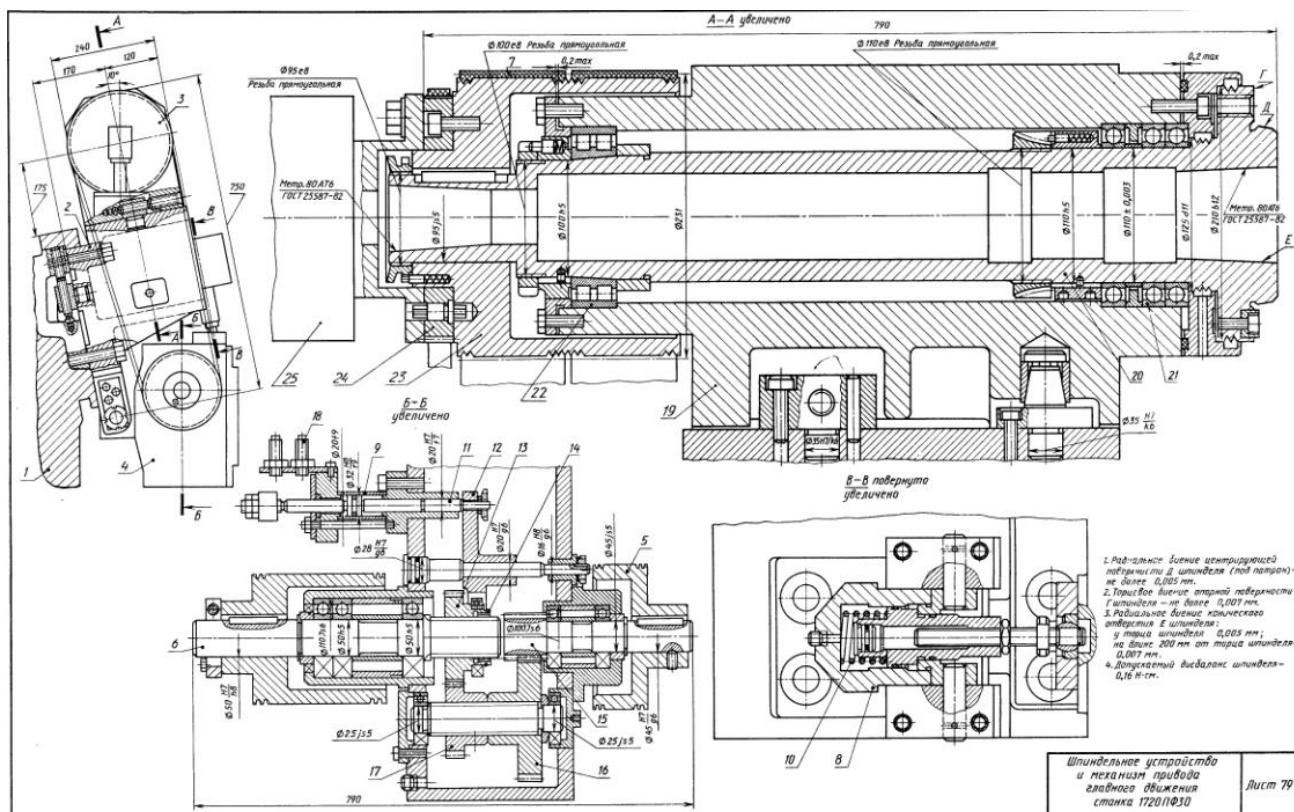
Шпиндельний механізм і механізм приводу головного руху верстата 1720ПФ30
